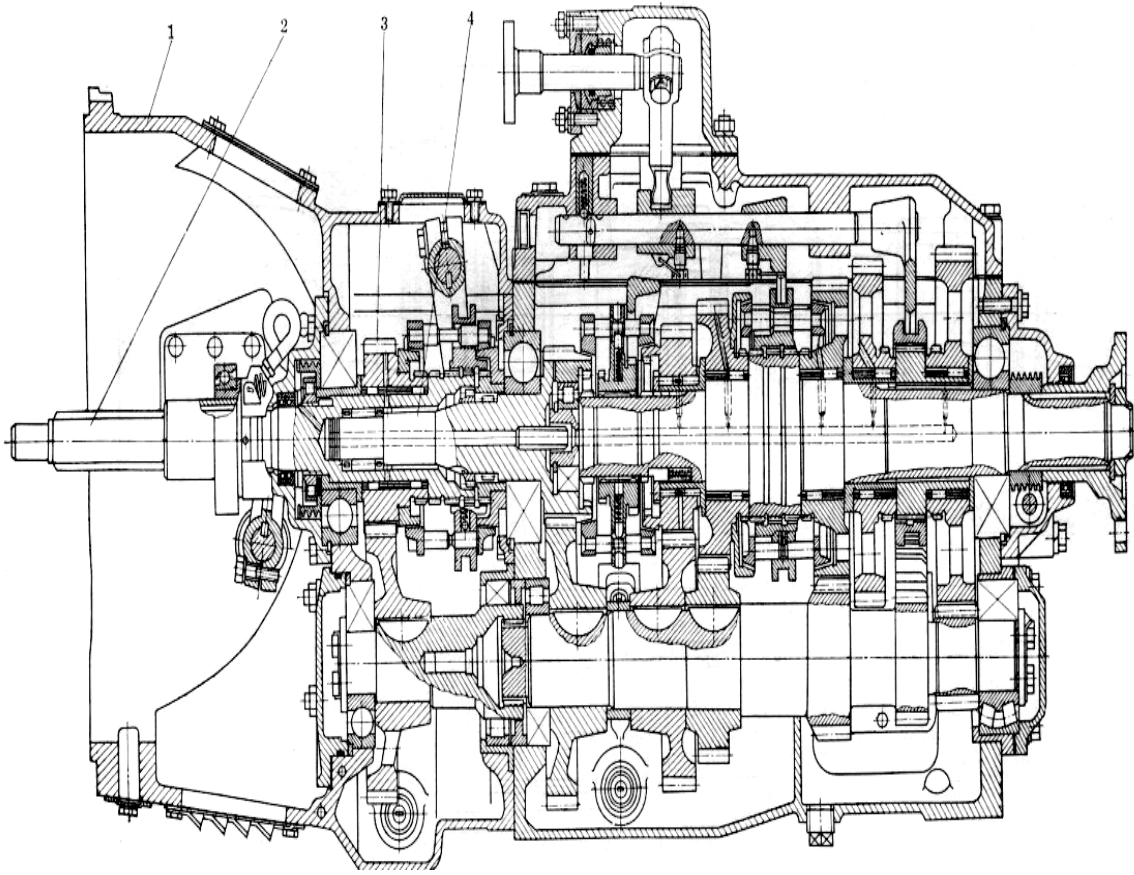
Десятиступенчатая коробка передач автомобиля КамАЗ-5320
